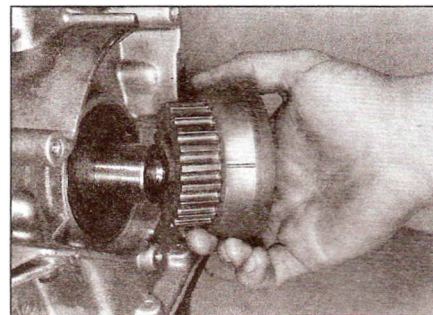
, б. ...затем снимите зубчатый шкив коленчатого вала
